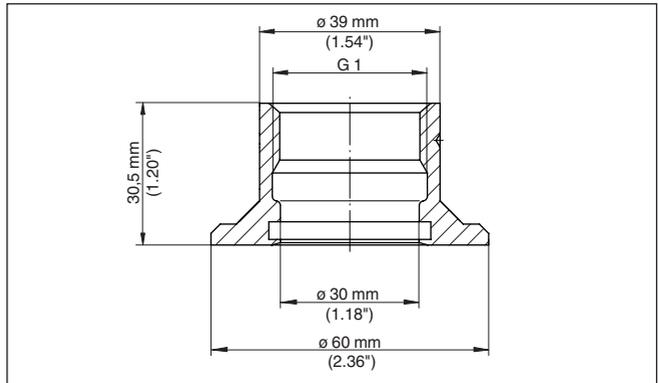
Dimensiones racor para soldar G1 (DIN 3852-X) - calidad alimentaria
